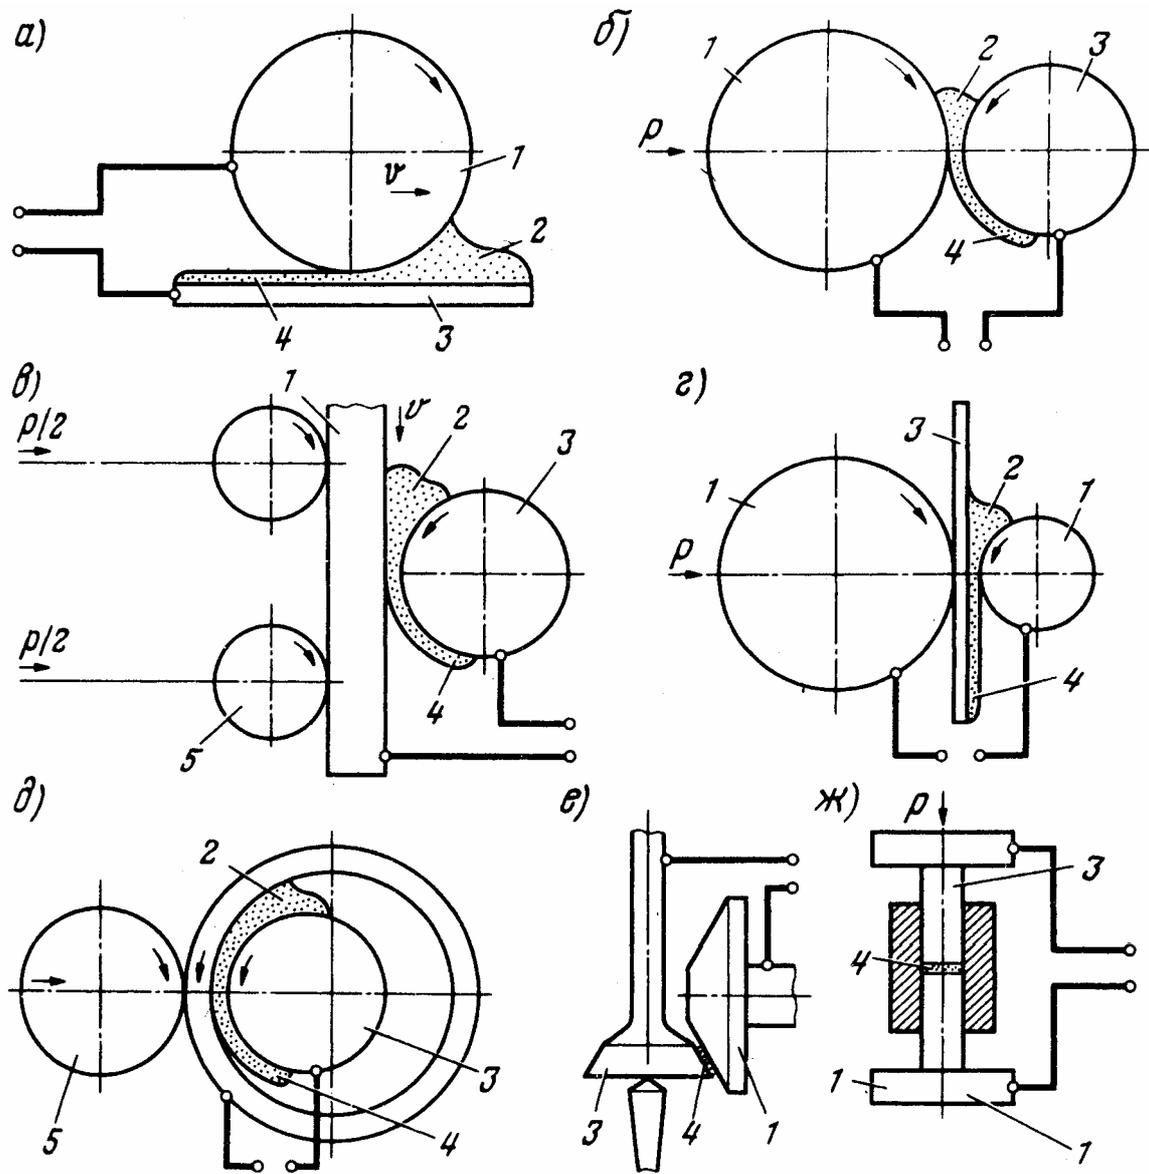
Схема электроконтактной приварки порошков на поверхности: а, г и ж – плоские; б, в и д – цилиндрические; е – коническую; 1 – электрод; 2 – порошок; 3 – деталь; 4 – покрытие; 5 – ролик
